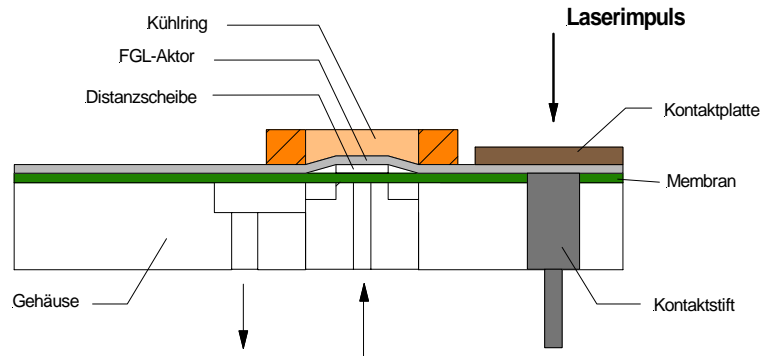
Elektrische Kontaktierung des FGL-Mikroventils durch Laserstrahlschweißen.
